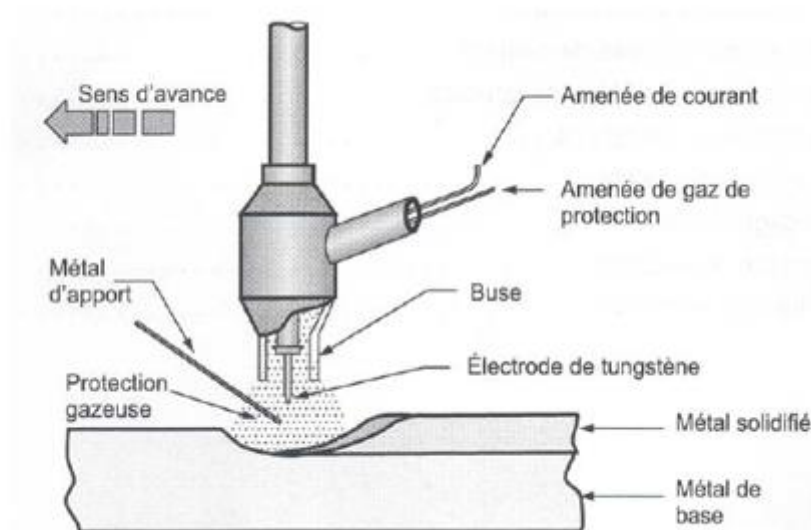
Procédé de soudage TIG.[7]
